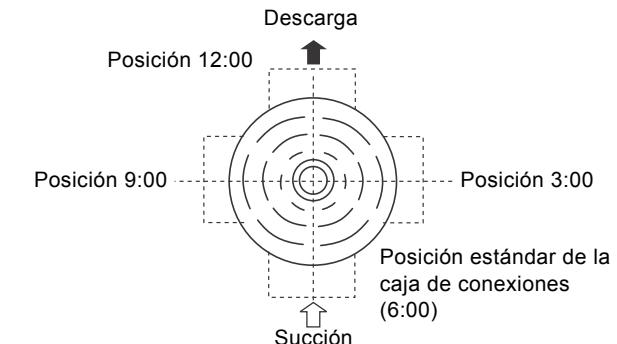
Posiciones de la caja de conexiones del motor (vista superior)
